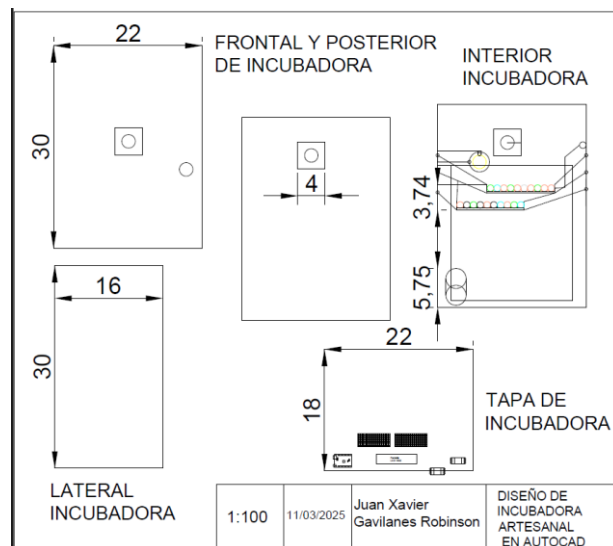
Plano estructural de la incubadora artesanal en AutoCAD.
